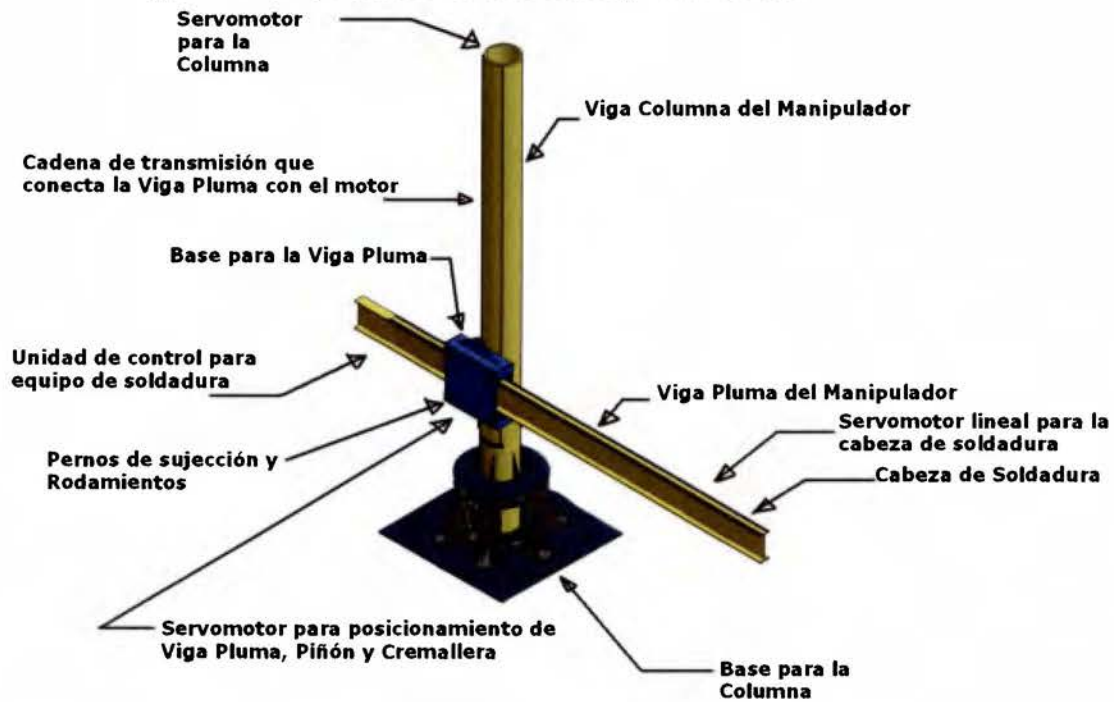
Diagrama de diseño para el manipulador de soldadura
